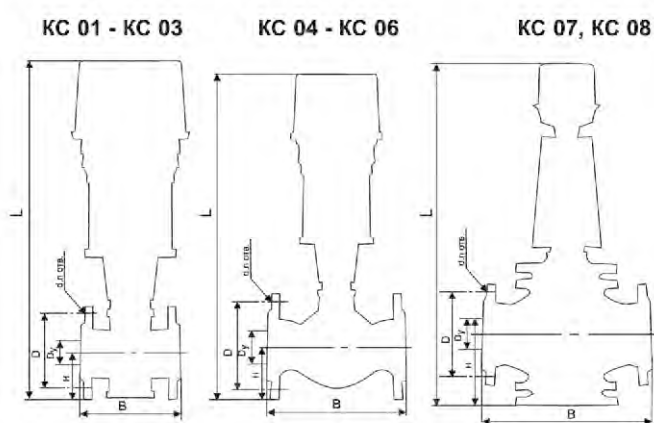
Габаритные и присоединительные размеры термомайзеров Р-2.Т.
